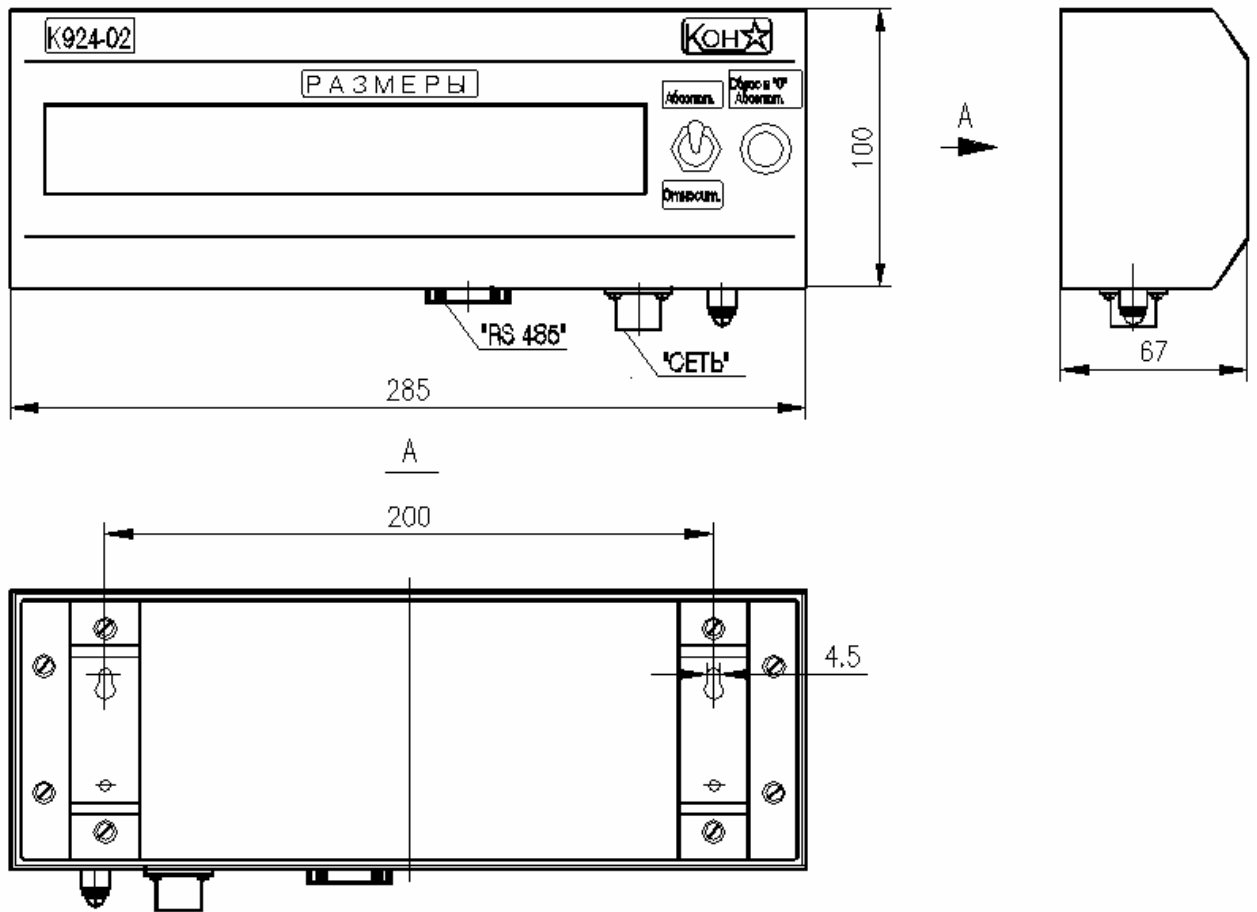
Внешний вид и габаритные размеры панели К924-02
